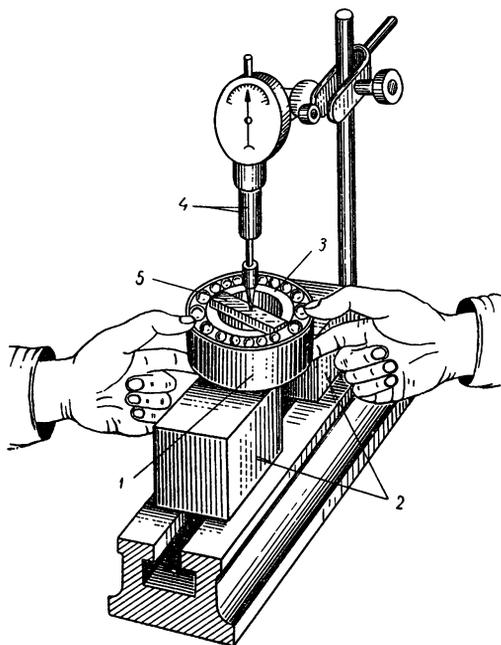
Проверка осевого разбега шарикоподшипника с помощью индикатора: 1 — наружное кольцо шарикоподшипника; 2 — контрольное приспособление; 3 — внутреннее кольцо шарикоподшипника, 4 — индикатор; 5 — пластина
